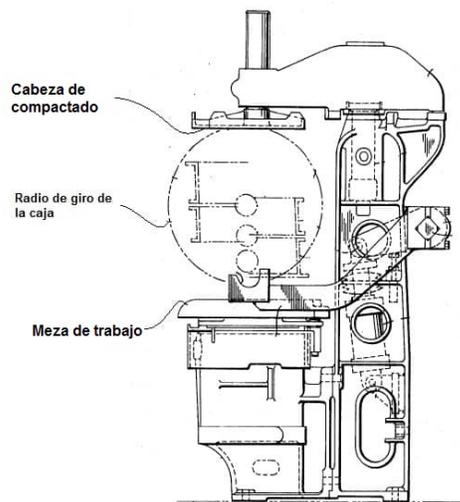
Squeeze head, jolt plate y radio de giro de la caja. [XII]
